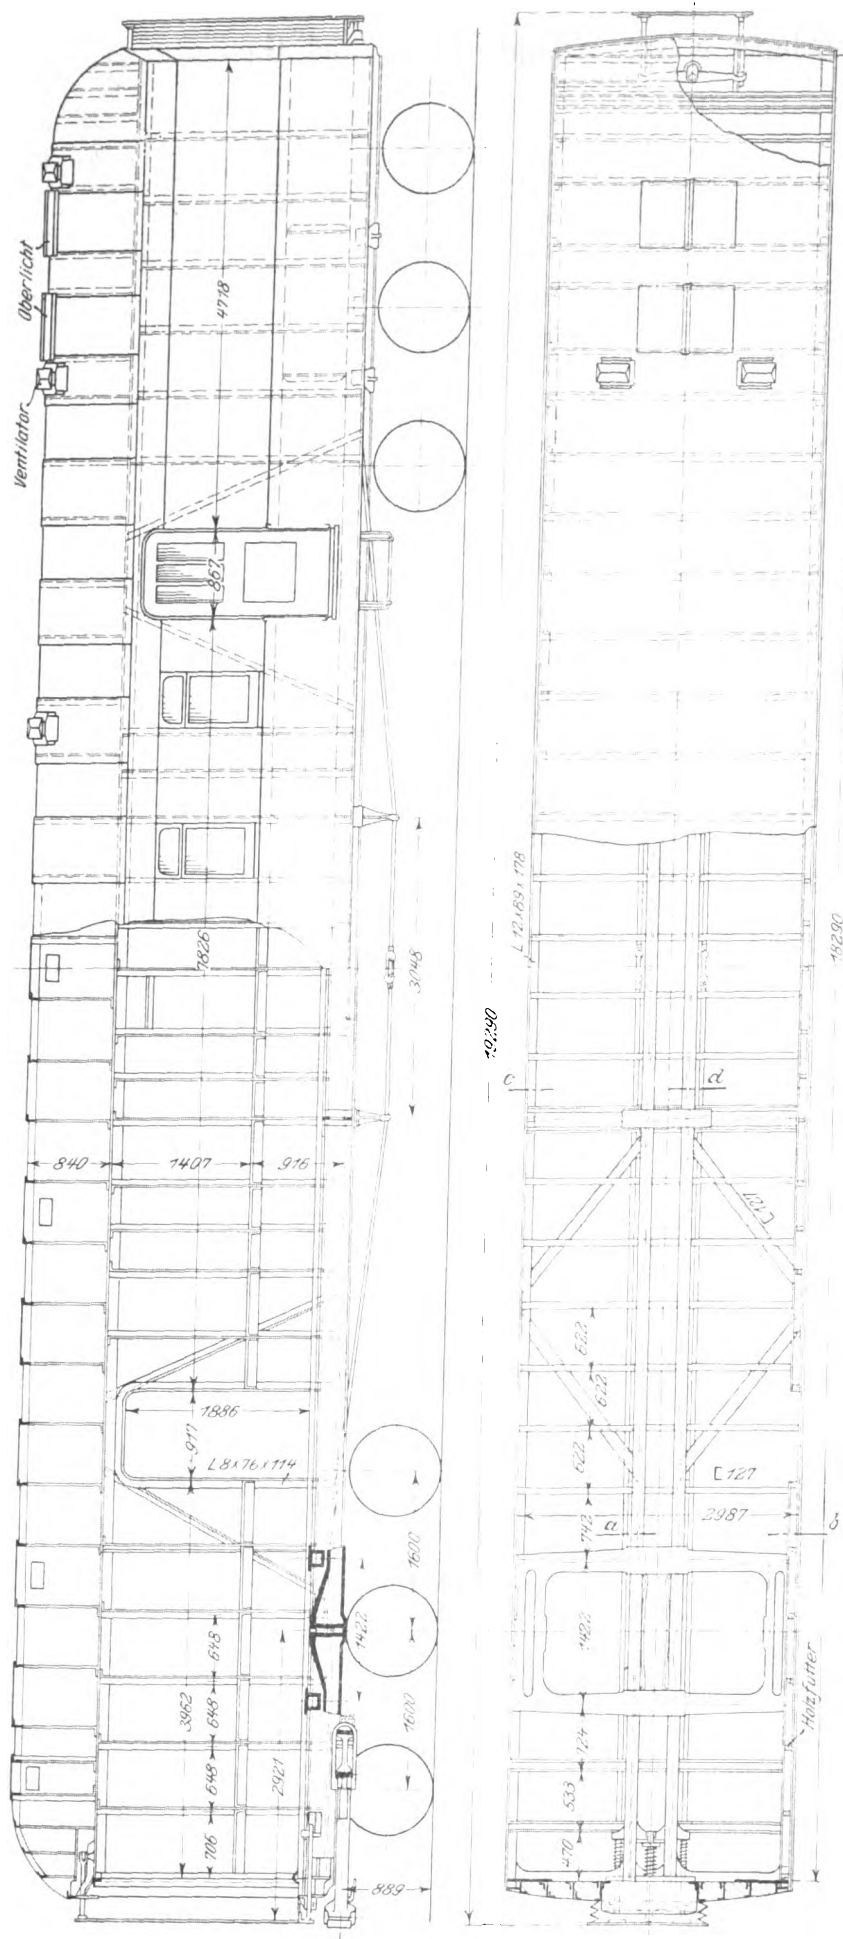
und 81. Längsschnitt und Grundriss.
